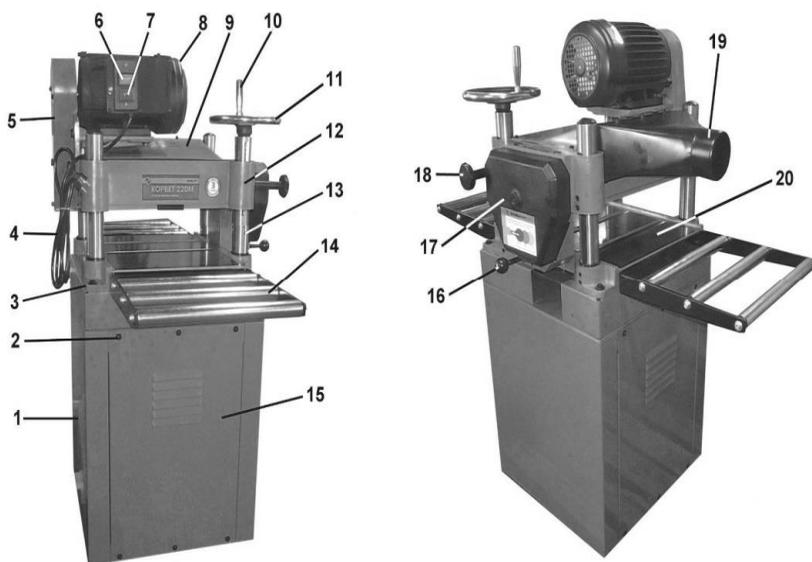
Устройство рейсмусового станка: 1 – основание; 2 – винт крепления; 3 – станина; 4 – шнур электрический с вилкой; 5 – кожух ременной передачи; 6–7 – кнопки включения-выключения; 8 – электродвигатель; 9 – верхний кожух; 10 – ручка маховика; 11 – маховик перемещения строгального вала; 12 – блок строгального вала; 13 – стойка; 14 – удлинитель стола; 15– съемная панель; 16 – ручка переключения скорости подачи; 17 – кожух редуктора автоподачи; 18 – ручка фиксации перемещения блока строгального вала; 19 – патрубок пылесборника; 20 – рабочий стол
